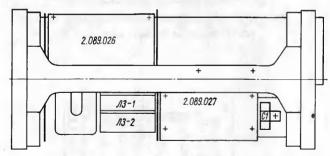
Схема расположения установочных элементов и печатных плат (вид сбоку)
